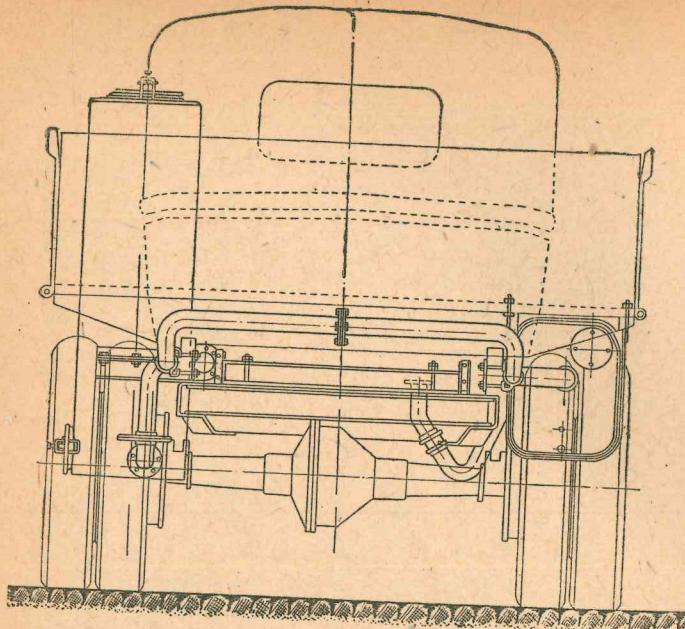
Автомобиль ГАЗ-АА, оборудованный древесноугольной установкой ЦНИИАТ-УГ-1. Вид сзади.
